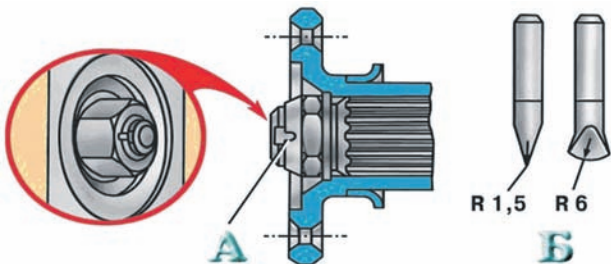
Стопоріння гайки вигином її кромки в паз валу і профіль інструменту: А – місце стопоріння; Б – профіль інструменту
